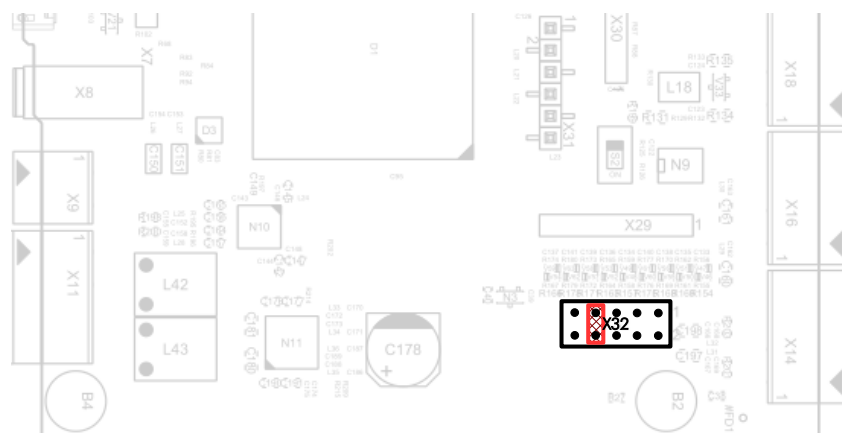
Jumperposition für Rücksetzen auf Werkseinstellungen während des Reboots
